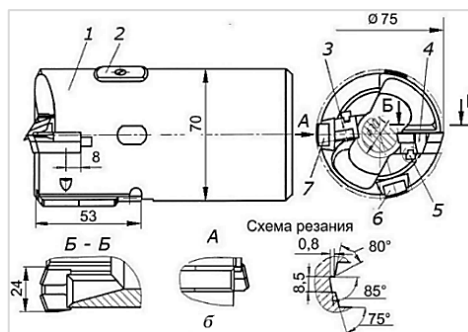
Двухрезцовая сверлильная головка $\varnothing 75$ мм: 1 – резец; 2 – упругая направляющая; 3 – проходной резец; 4 – калибрующий резец; 5 – координатная шпонка; 6 – направляющая шпонка опорная; 7 – направляющая шпонка упорная
